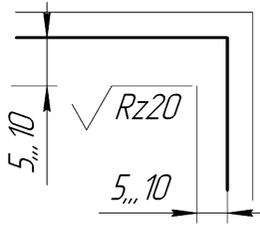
Пример обозначения шероховатости поверхностей, одинаковой для всех поверхностей детали
